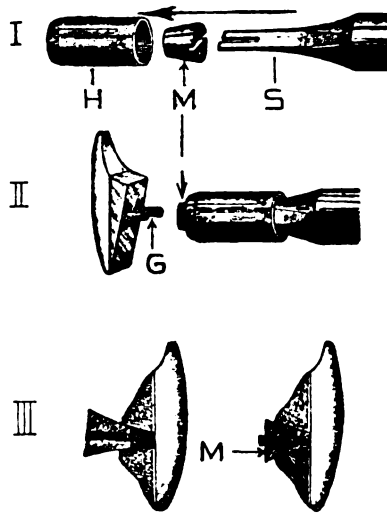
I. Die in den „Universal-Schraubenschlüssel“ eingearbeiteten Bryant-Schraubenzieher (S) und Hülse (H) mit einer Bryant-Mutter (M).
